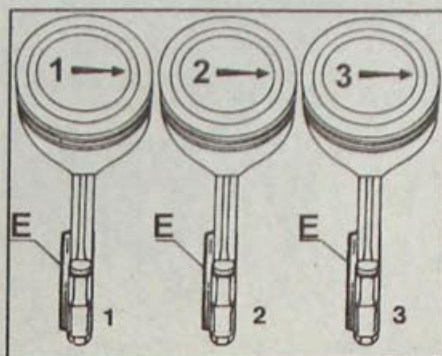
Поршни 1, 2 и 3 цилиндров с выступом (E), смещенным к задней части двигателя
